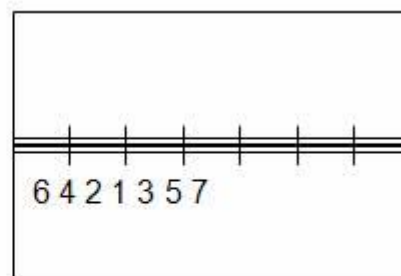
Обратнo-ступенчатая сварка
